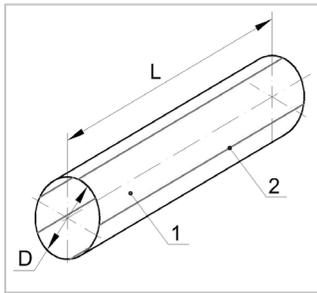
Схема сварной обечайки котла железнодорожной вагонцистерны, сваренной из листового полотнища: 1 – лист; 2 – продольный сварной шов; D – внутренний диаметр обечайки; L – длина обечайки (длина продольного сварного шва)
